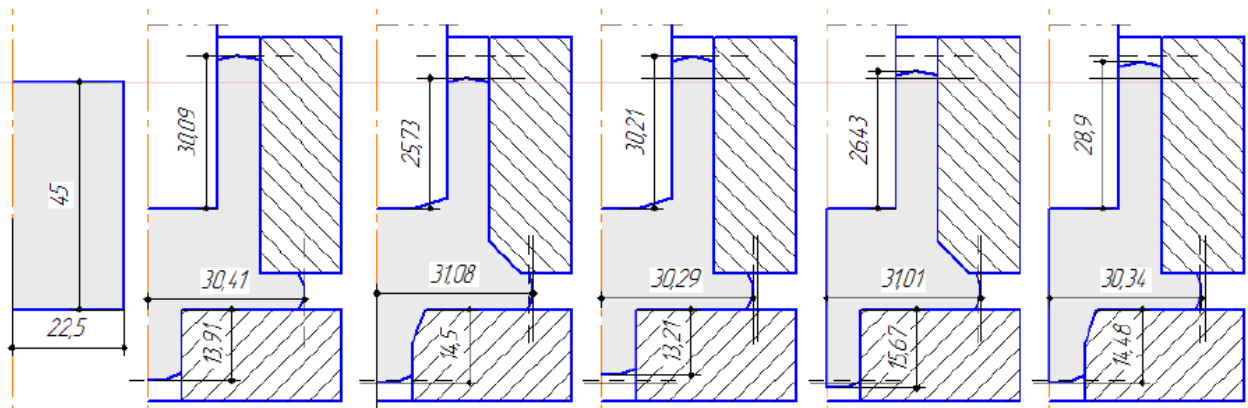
Вплив фасок інструменту на формозміну заготовки
